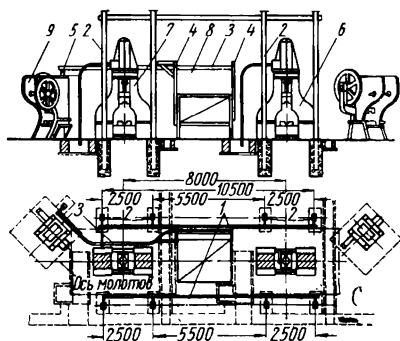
Схема расположения однорельсовых путей в агрегатах тяжелых штамповочных молотов: 1 — однорельсовый путь для подвешивания и перемещения «сокола»; 2 — металлические стойки; 3 — однорельсовый путь для межоперационной передачи заготовок; 4 и 5 — металлические стойки; 6 и 7 — штамповочные молоты; 8 — нагревательная печь; 9 — обрезающий пресс
